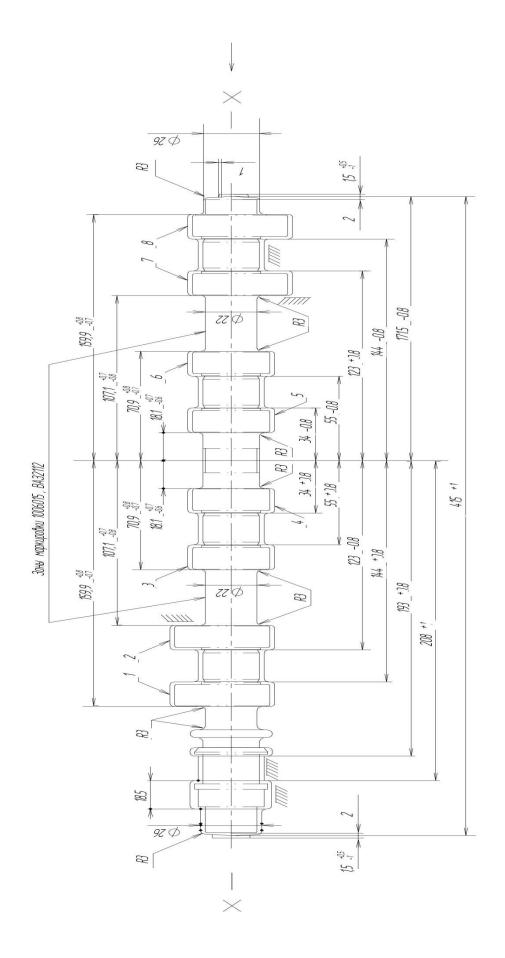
Общий вид заготовки детали - «Распредвал»
